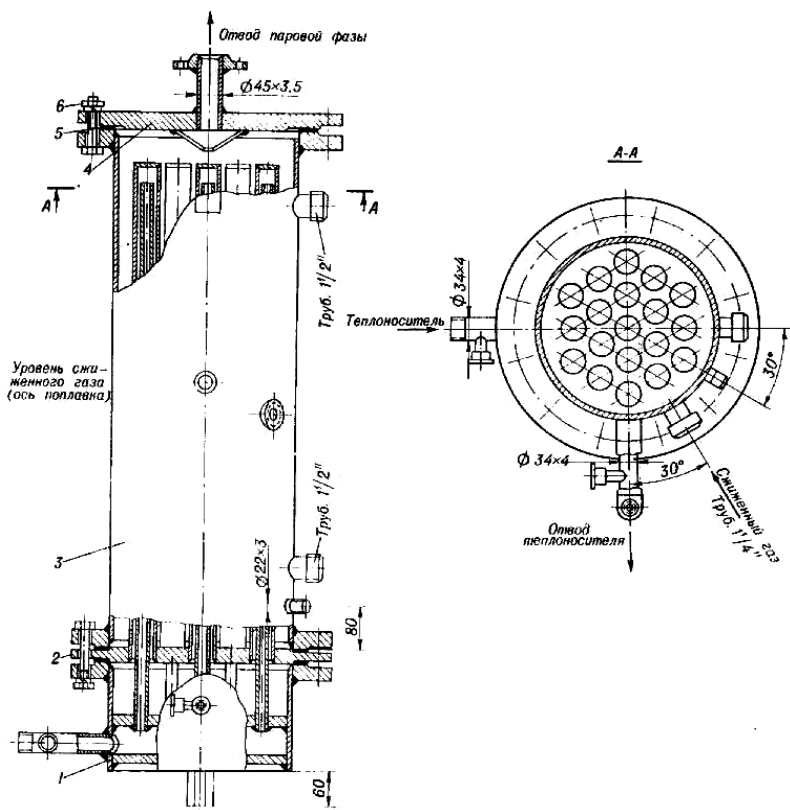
Кожухообразный вертикальный испаритель с нижними трубными решетками:
